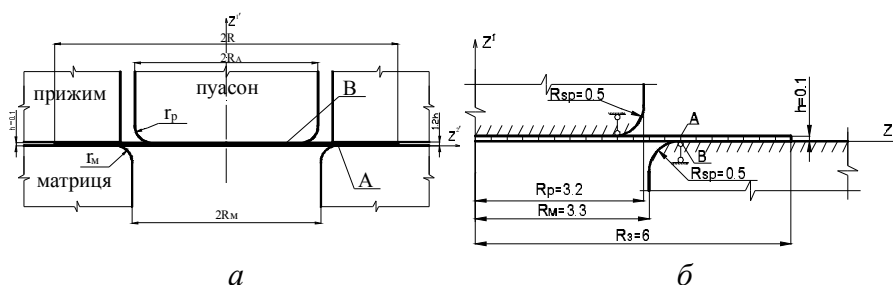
Стенд витяжки круглої пластини в циліндричний стакан (а), розрахункова схема процесу витяжки (б)
